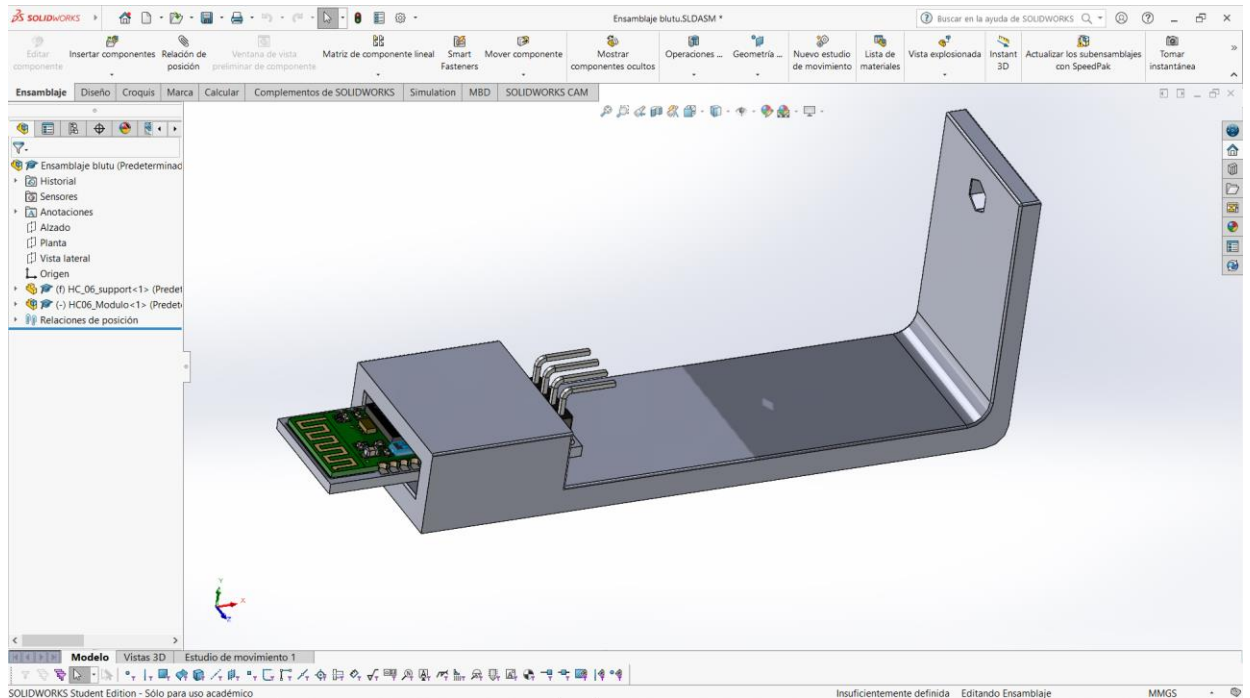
Diseño de soportes de sensor de ultrasonido en el CAD SolidWorks.
